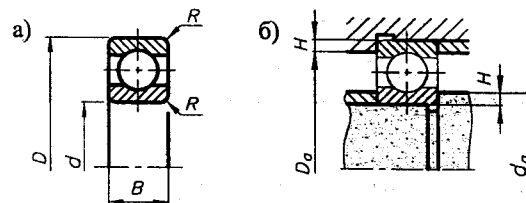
Размеры подшипников для их установки: а) габаритные размеры; б) установочные размеры (размеры заплеchkов)
